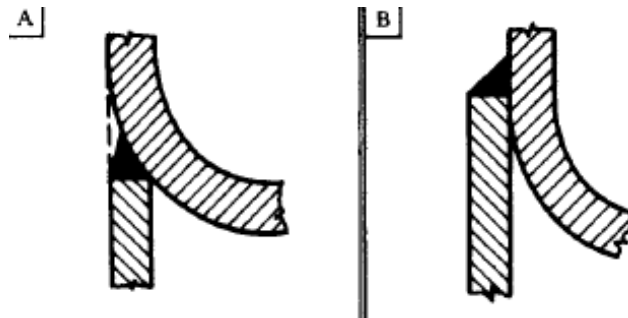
Tipos de soldadura del faldón al cabezal [14]
